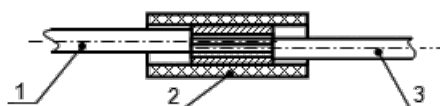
Общий вид корпуса гильзы в разрезе
